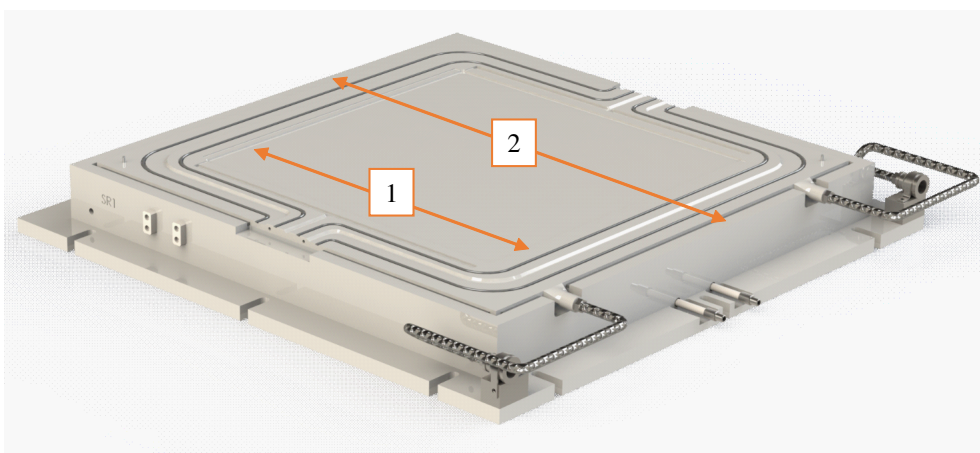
Dimensions principales de la peau chauffante du démonstrateur industriel
